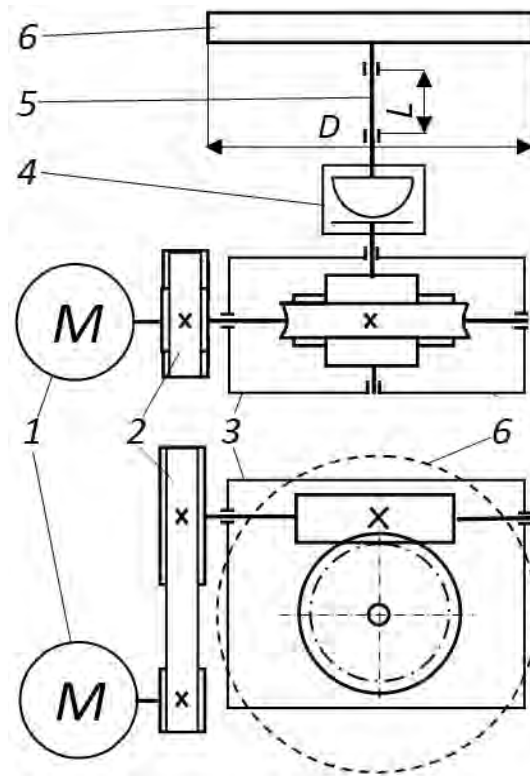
Схема привода питателя (фронтальный вид и вид сверху): 1 – асинхронный электродвигатель; 2 – ременная передача; 3 – редуктор червячный с вертикальным расположением ведомого вала (с боковым расположением червяка); 4 – зубчатая муфта; 5 – приводной вал с опорами, которые крепятся на горизонтальных поверхностях (параллельных рабочей поверхности питателя); 6 – диск питателя
